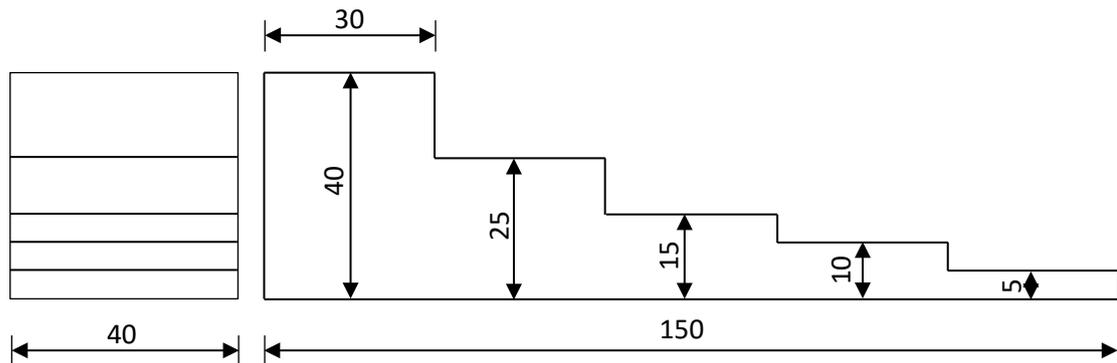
Dimensões do bloco padrão a ser utilizado para calibração dos instrumentos de medição, cotas em [mm].
